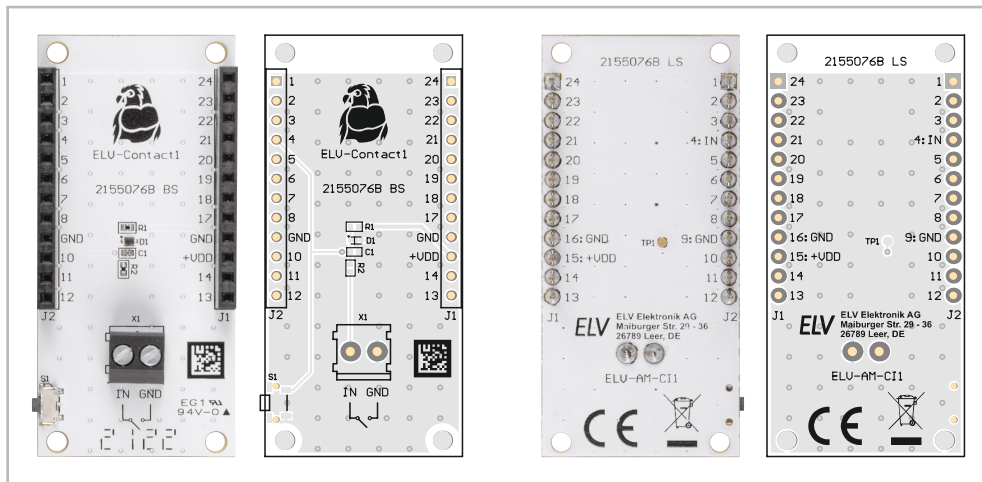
Platinenfotos und zugehörige Bestückungsdrucke des ELV-Contact1
